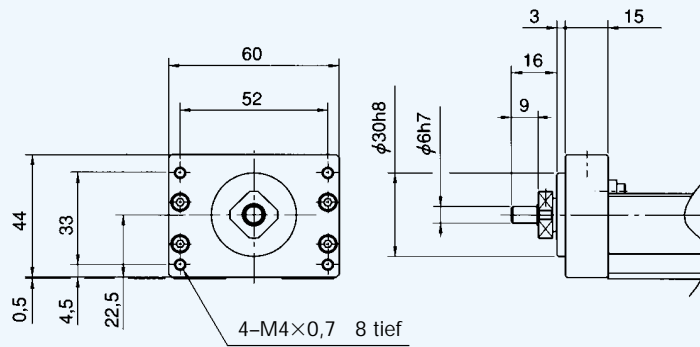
KR33 Housing A ohne Motorflansch (Kennziffer □□30)
